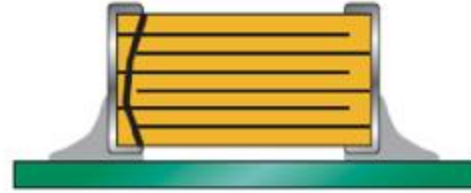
Detail rohu rozbroušeného komponentu 1210 s Board Flex defektem.
